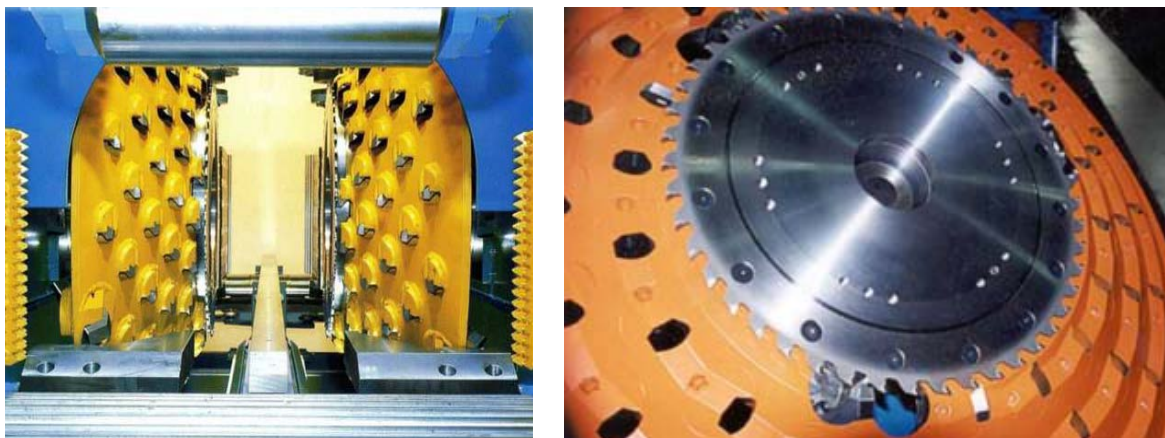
Торцово-конические фрезы фрезерно-брусующих станков
